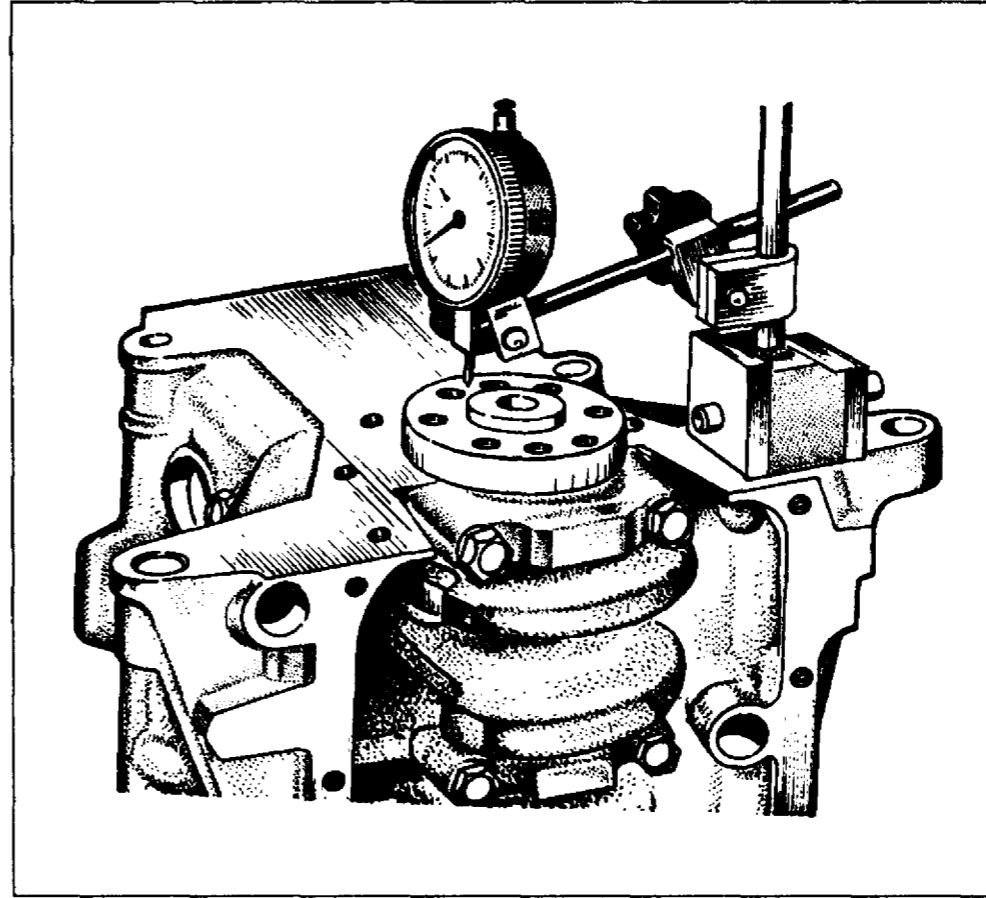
Проверка осевого свободного хода коленчатого вала
